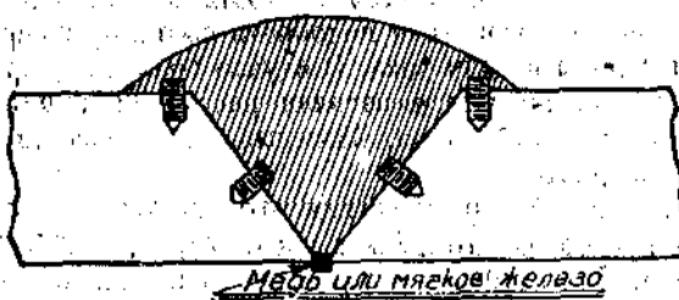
Подготовка чугуна к сварке с полоской из латуни или мягкого железа.
